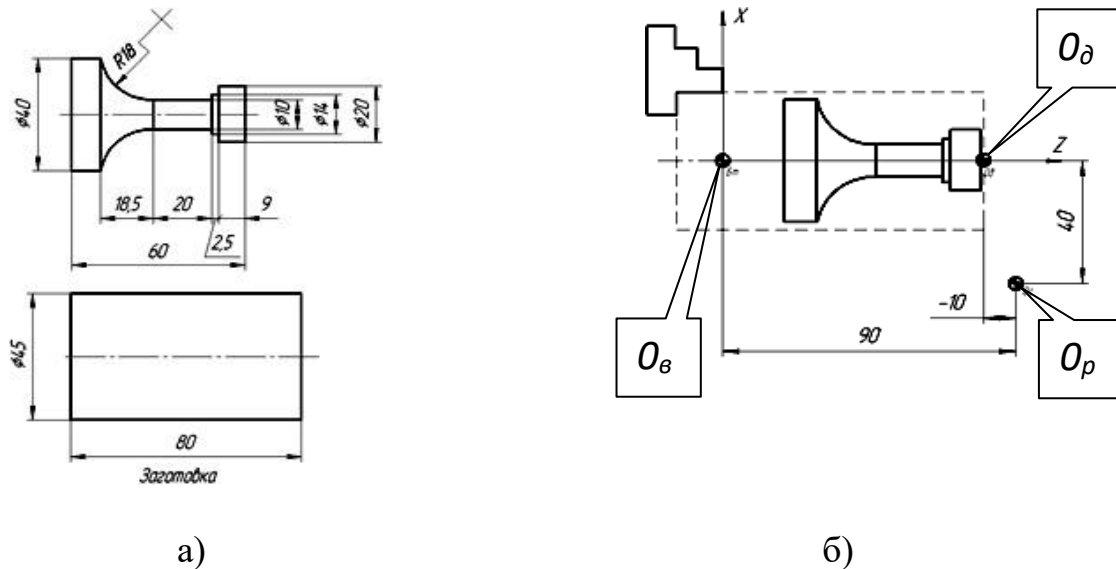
Робочий кресленик а – пропонованої деталі та б – схема налаштування симулятора
